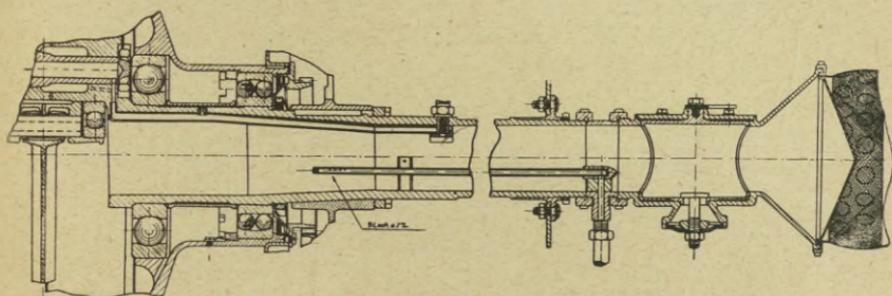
Vergaser des 100 PS Gnom-Motors mit Winterdüse.
